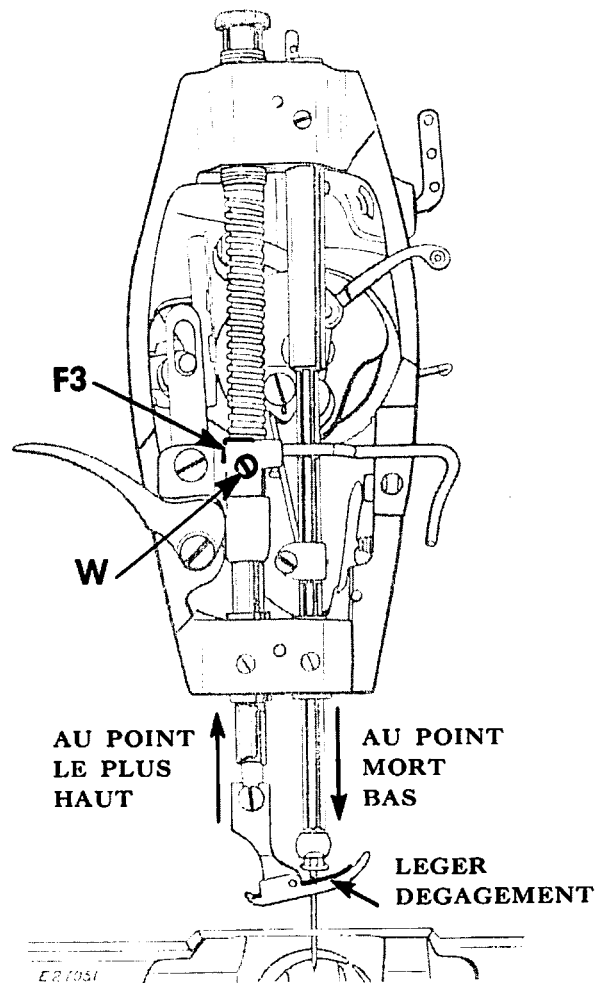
Vérification de la hauteur de la barre du presseur relevée à fond
